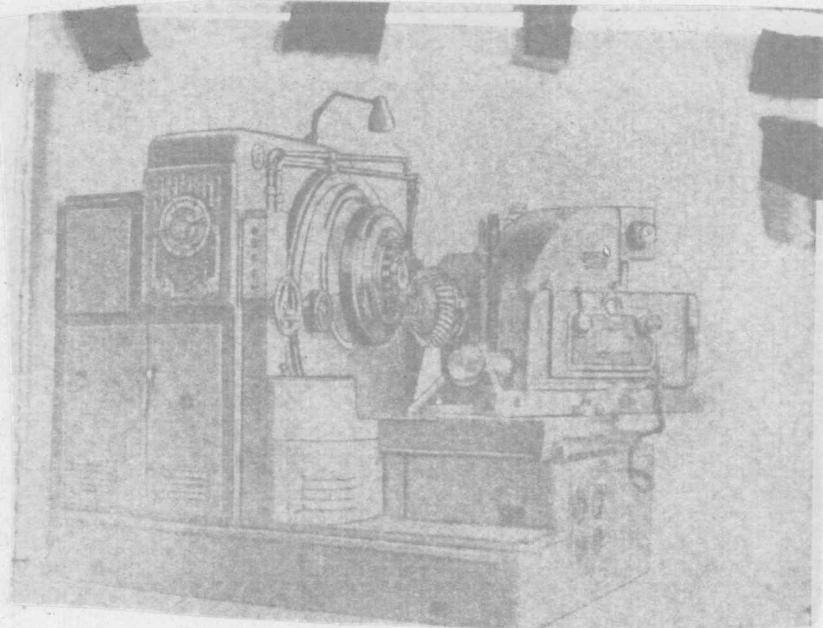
、切削螺旋伞齿轮用的 528 型高速半自动机床
